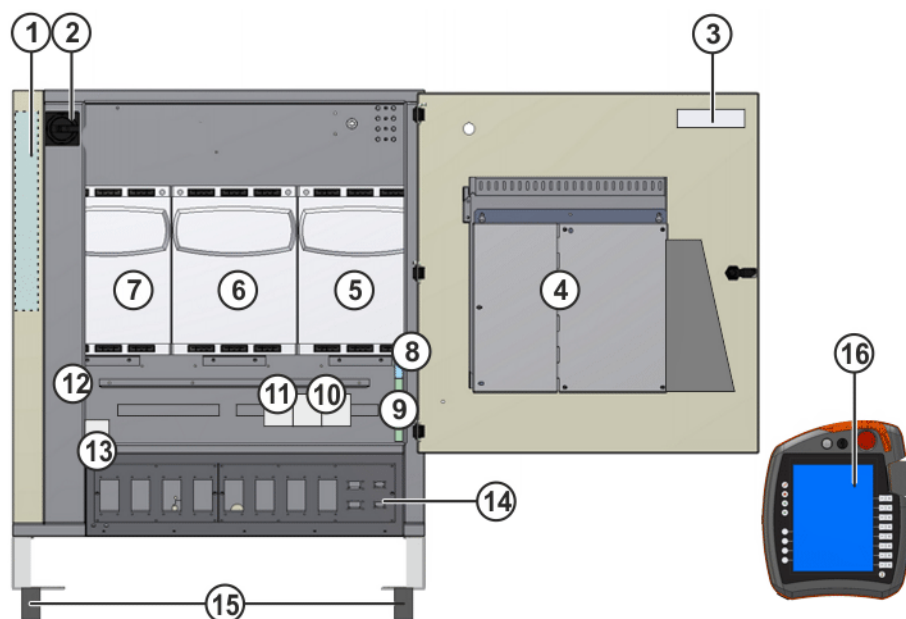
Vista general de la unidad de control del robot, vista frontal
